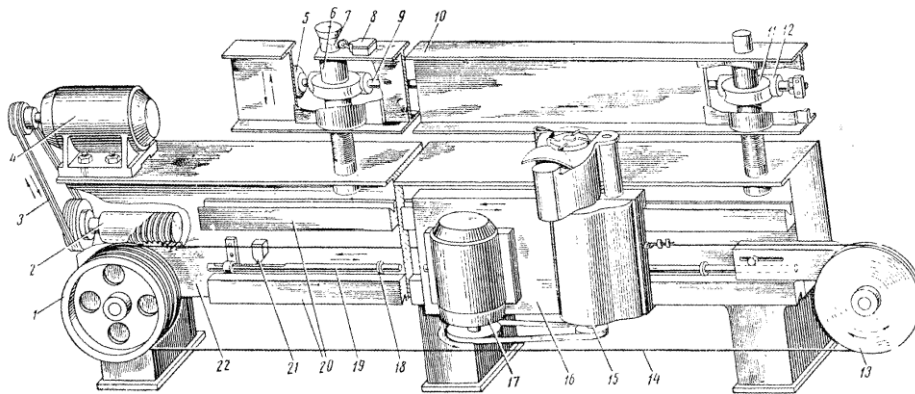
Схема кромкофугувального верстата: 1 - струмковий барабан; 2 - черв'ячний редуктор; 3 - пасова передача; 4 - електродвигун супорта; 5 - електродвигун привода притисків; 6 - гайка; 7 - стійка; 8 - кінцевий вимикач; 9 - вал привода притиску; 10 - притиск; 11 - черв'ячні шестірни; 12 - черв'як; 13 - натяжний блок; 14 - трос; 15 - шпиндель; 16 - супорт; 17 - електродвигун шпинделя; 18 - кільця; 19 - стрижень; 20 - напрямні; 21 - кінцевий вимикач; 22 - станина
